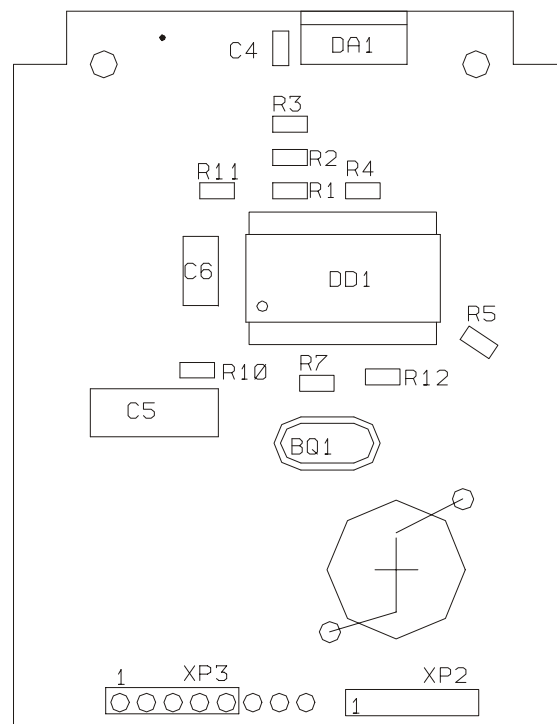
Сборочный чертеж блока датчика ФСТ (СхНх). Сторона пайки.
